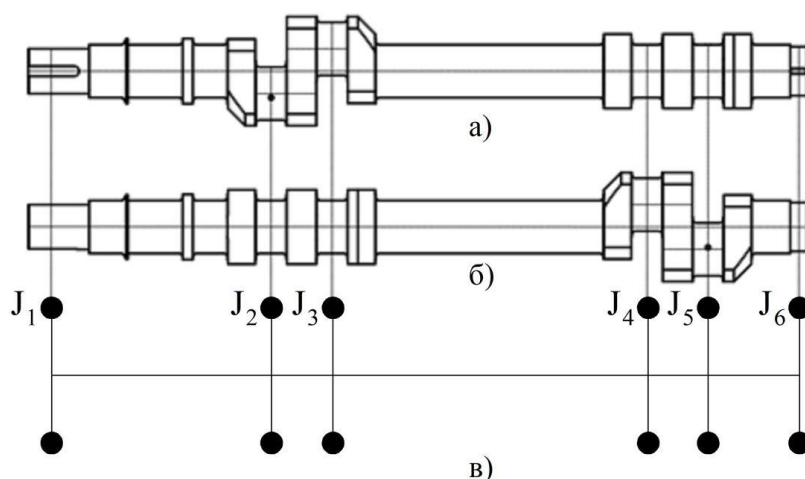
коленчатый вал четырёхрядного поршневого компрессора для базы 4М16
